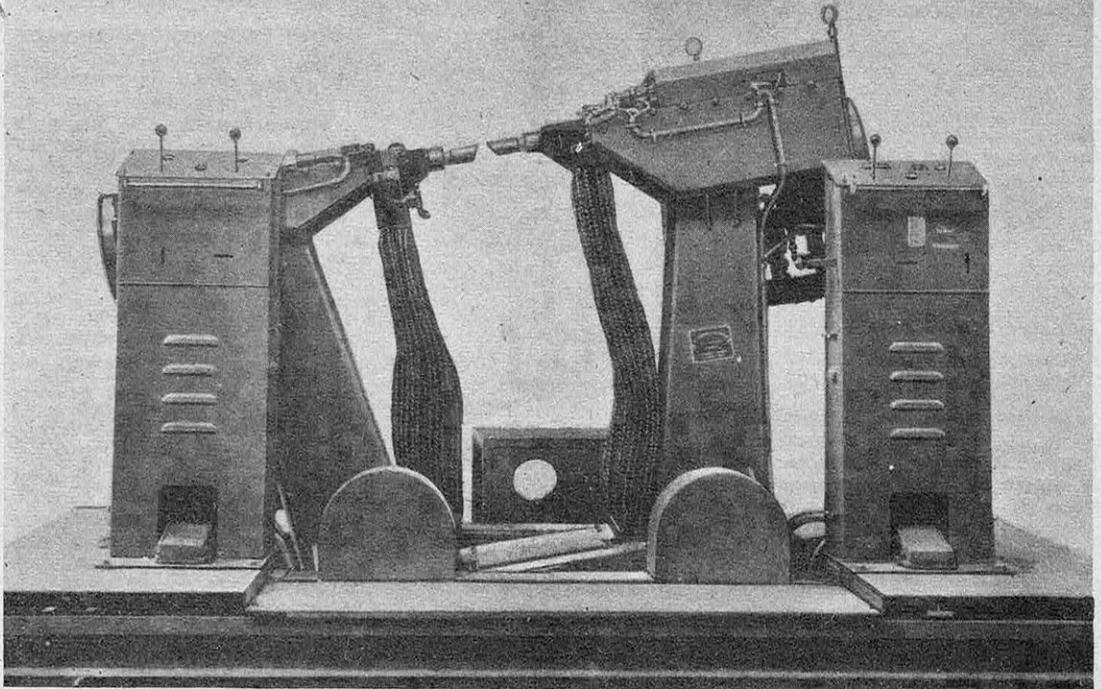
MACHINE A SOUDER PAR POINTS LES ALLIAGES LÉGERS
